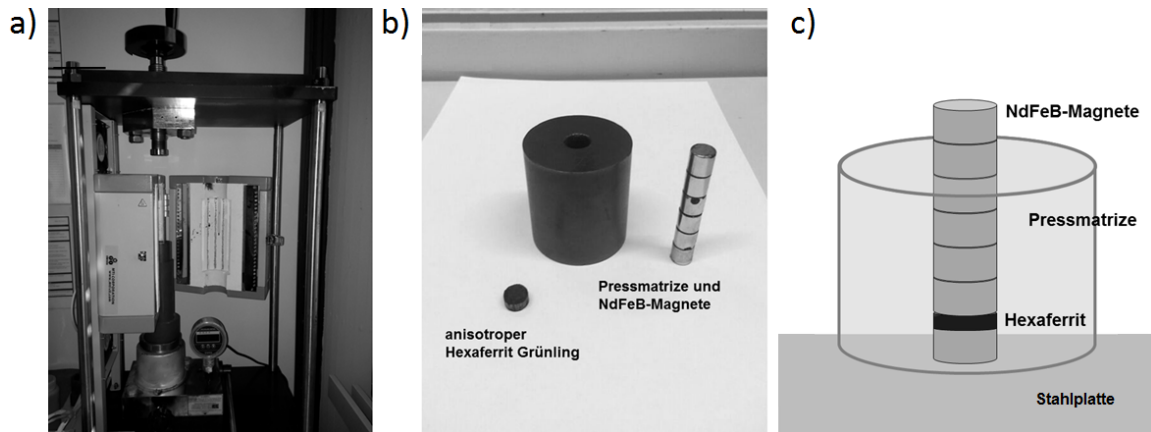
a) Uniaxiale Hydraulikpresse der MTI Corporation. b) Pressmatrize mit NdFeB-Magneten zur Felderzeugung und gepresster Hexaferritgrünling. c) Schematischer Aufbau zur Magnetfelderzeugung innerhalb der Pressmatrize.
